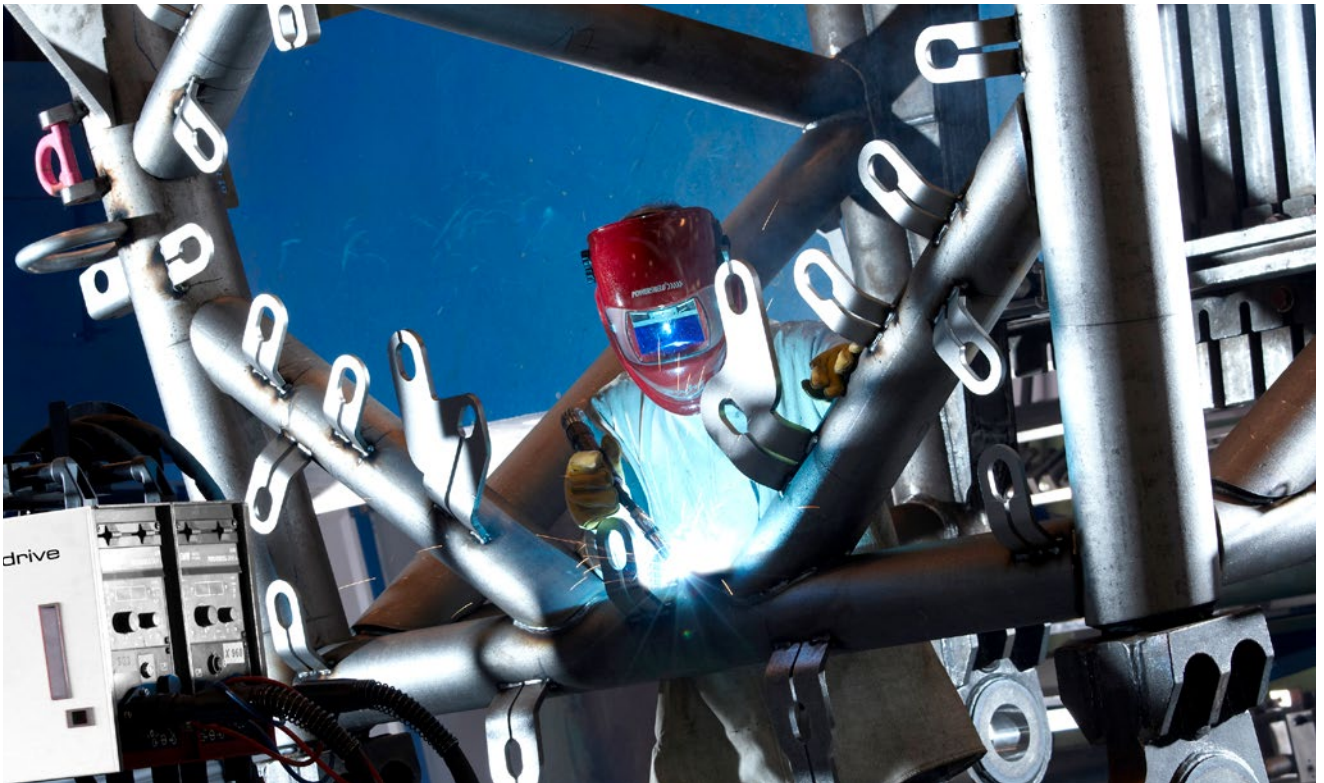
MSG-Schweißen hochfester Stähle im Kranbau mit Fülldrähten
